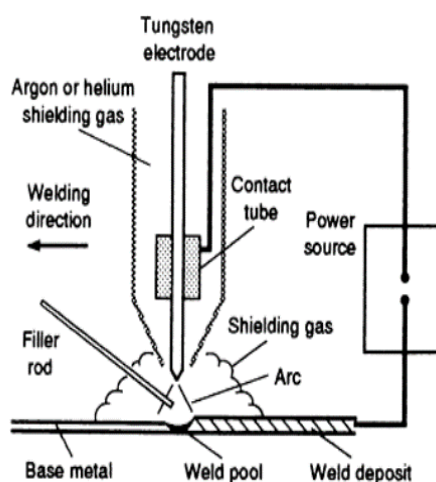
Esquema simple de proceso de soldadura GTAW.
